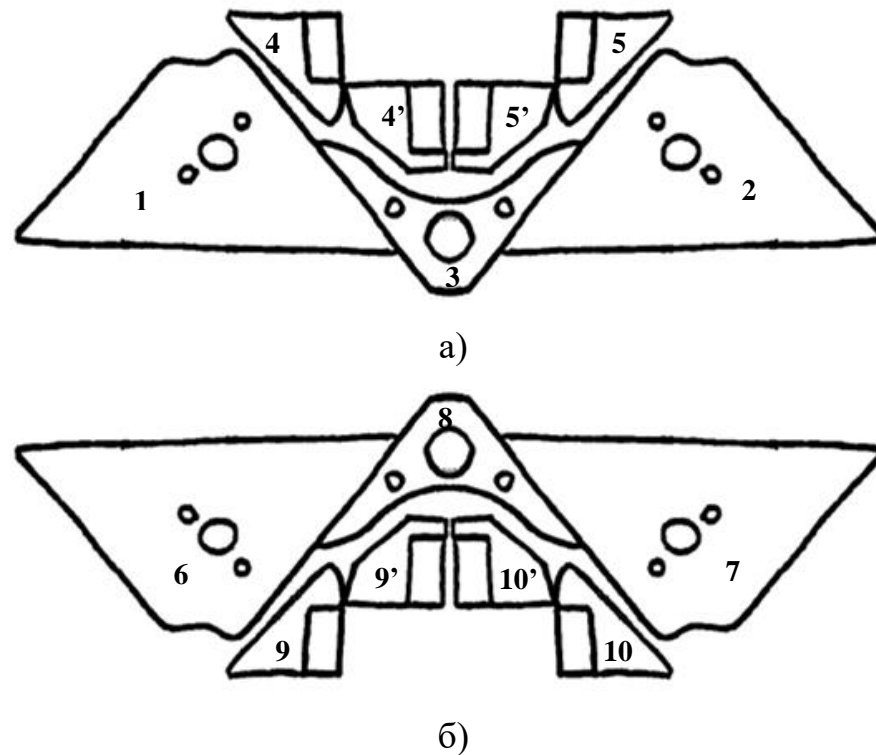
Схема голкових замків плоскофангової машини: а – задній корпус корпус; б – передній корпус
